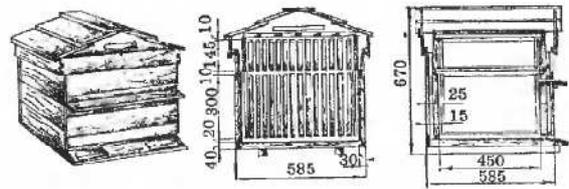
14-рамочный утепленный улей: а — общий вид; б — поперечный и продольный разрез
